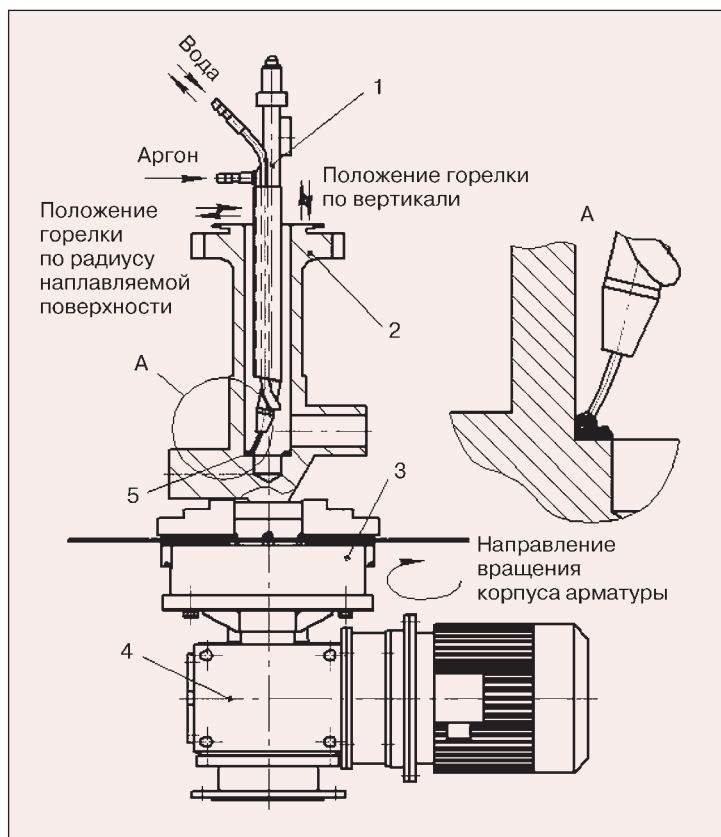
Схема наплавки корпуса арматуры: 1 — мундштук; 2 — корпус арматуры; 3 — зажимное устройство; 4 — вращатель; 5 — наплавляемая поверхность
